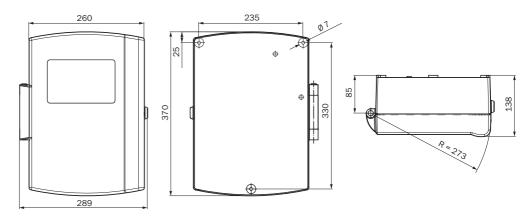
Dimensiones de la unidad de evaluación del GM35, versión: caja de chapa
